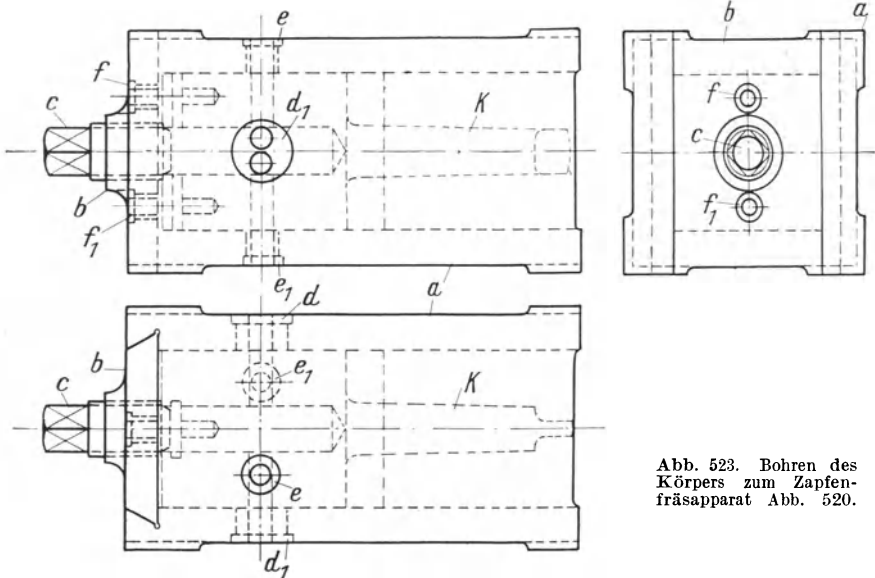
Bohren des Körpers zum Zapfenfräsapparat Abb. 520.
